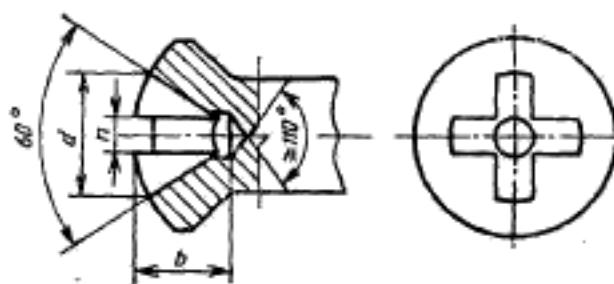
Головка с внутренним крестообразным шлицем
